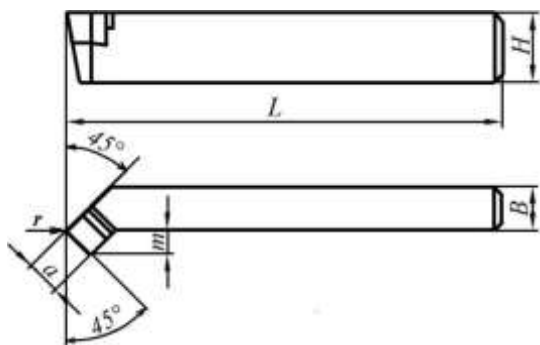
Резец токарный проходной, отогнутый с пластинками из твердого сплава (ГОСТ18877-73)
